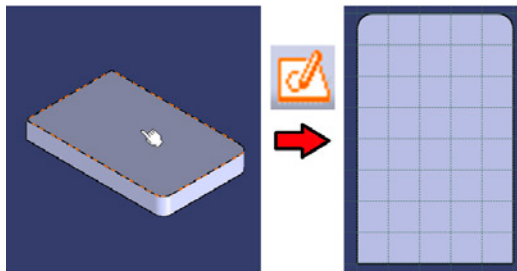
Bauteiloberfläche als Stützelement für eine neue Sketch
